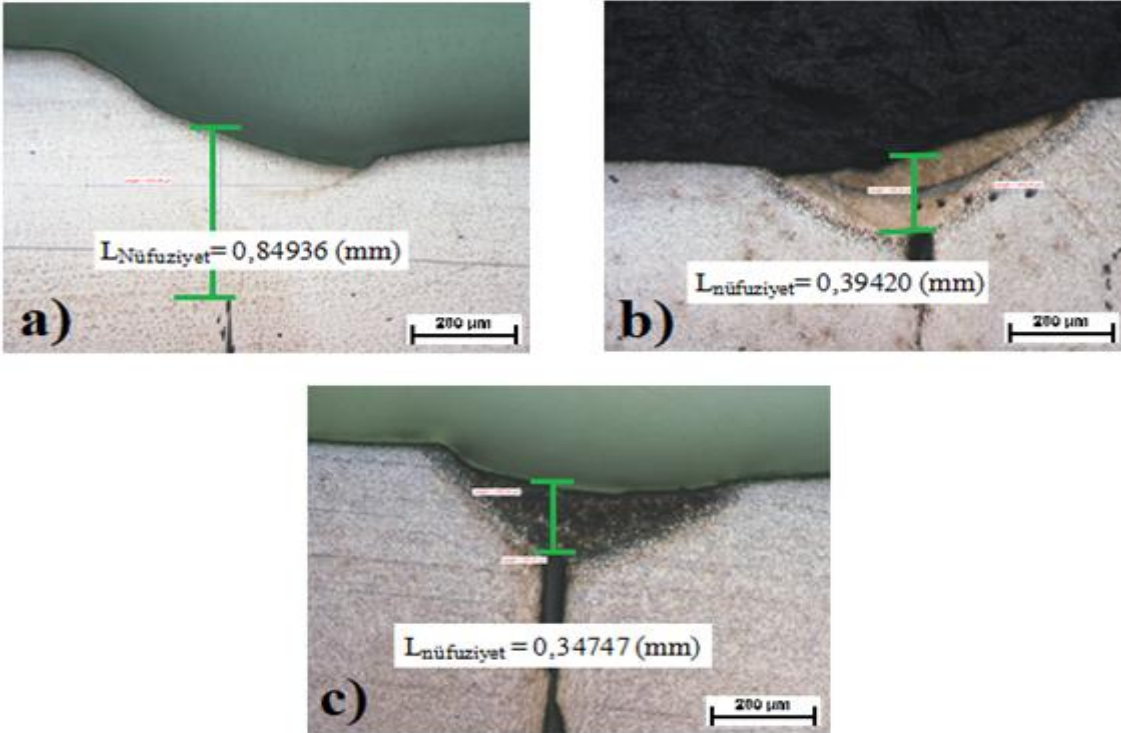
'te kaynak ilerleme hızının kaynak kesitindeki nüfuziyete olan etkisinin ters orantılı olduğunu görmekteyiz. Malzemenin cinsine bakılmaksızın kaynak ilerleme hızının yükek bir değerde seçilmesi sonucu her halükarda hem kaynak dikişinde hemde kaynak kesitinde bir azalma görülecek ve yapılan kaynağın istenilen kalitedeki özellikleri vermeyeceği anlaşılmaktadır.
